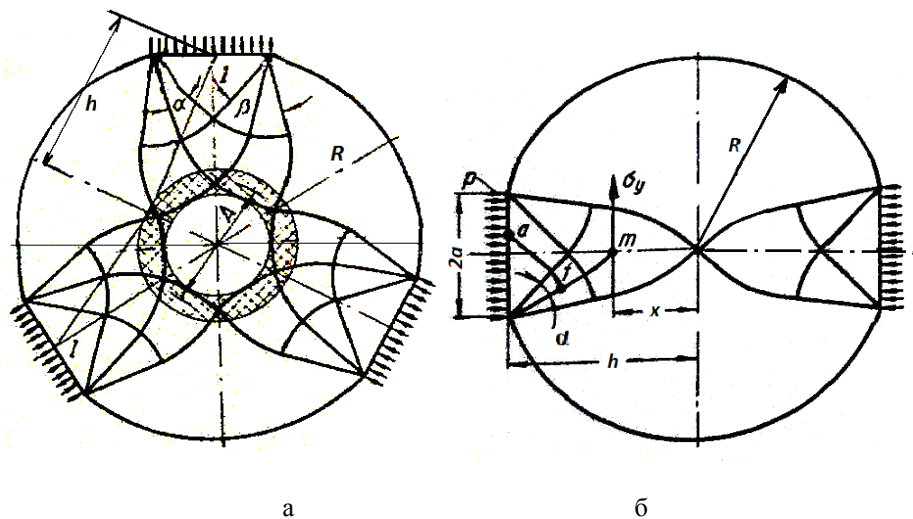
Сетка линий скольжения : а – для двухвалковой схемы прокатки; б – для трехвалковой схемы прокатки
